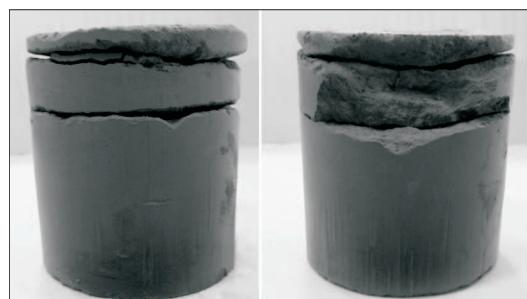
Образцы-цилиндры полусухого прессования из суглинка с формовочной влажностью 5,7 %
